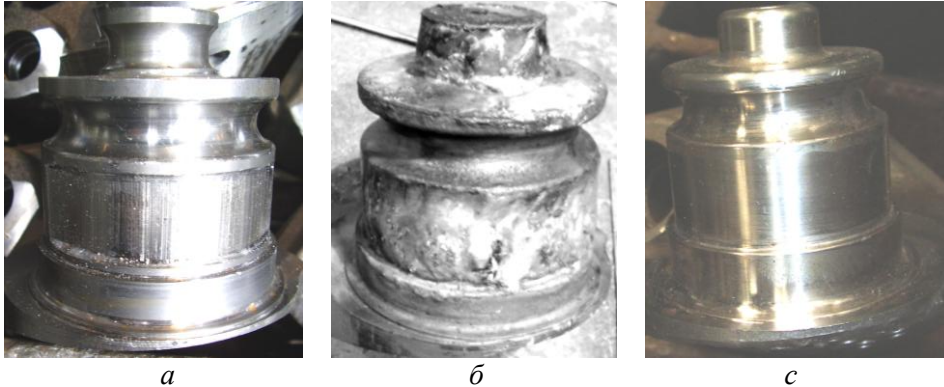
Загальний вигляд заготовки цапфи лапи тришарошкового долота 215,9 FS3 UT275 із навантаженої сторони, на якій є ділянка периферійного підшипника що наплавляється зносостійким матеріалом:
